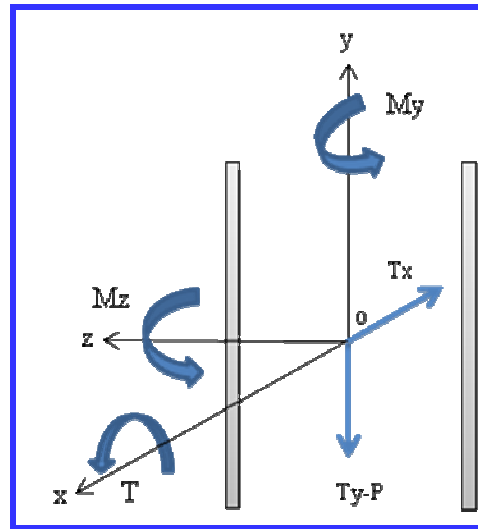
Centro de gravedad de la soldadura. [Fuente propia]
